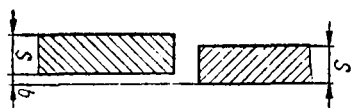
Схема смещения кромок элементов при сварке.
